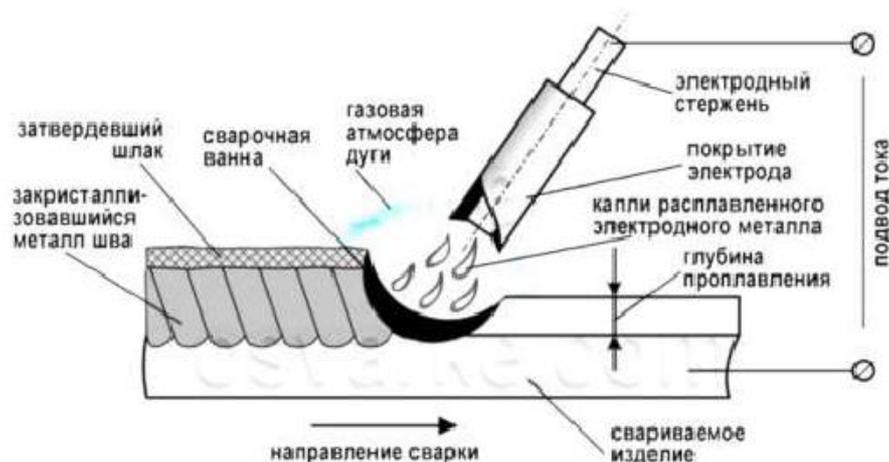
Схема сварки покрытым металлическим электродом
